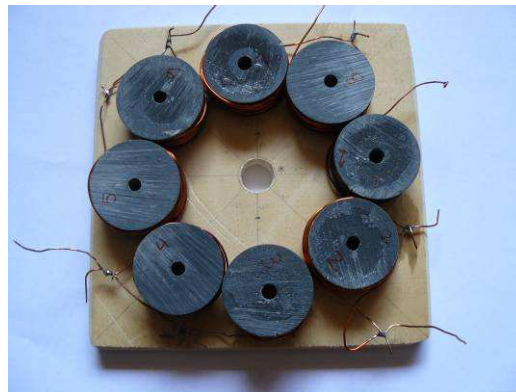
Bobines enganxades, connectades i soldades
